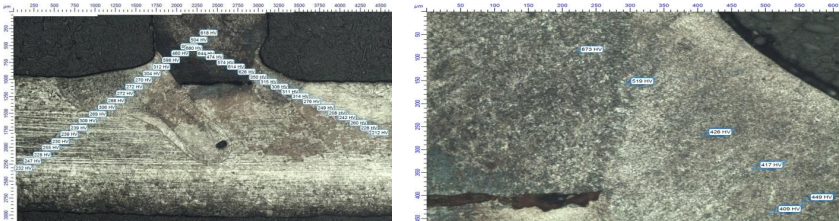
Сварное соединение стали 12X18H10T полученное при помощи лазерной сварки, правая часть – 1200Вт, левая – 900Вт
